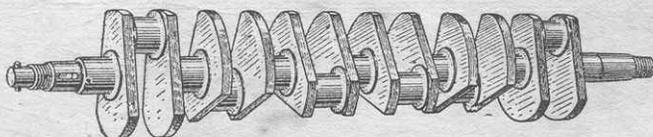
Коленчатый вал шестицилиндрового двигателя с противовесами 18/70 с. автомобиля Ауди, монтируемый на семи коренных подшипниках.
